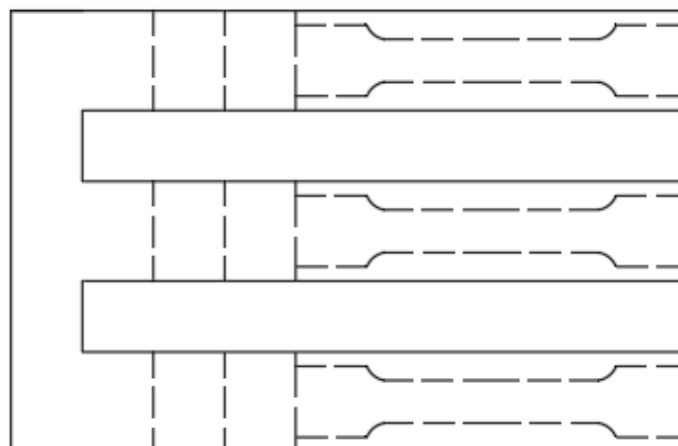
Moldura para la obtención de las probetas cilíndricas.
